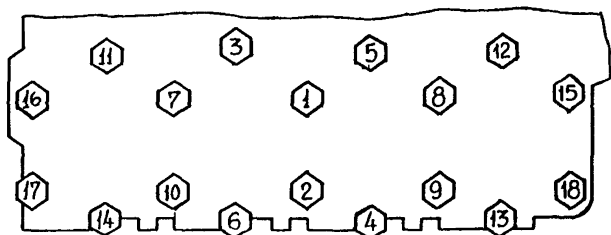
Порядок затяжки гаек головки цилиндров двигателя ЗМЗ-53-07
